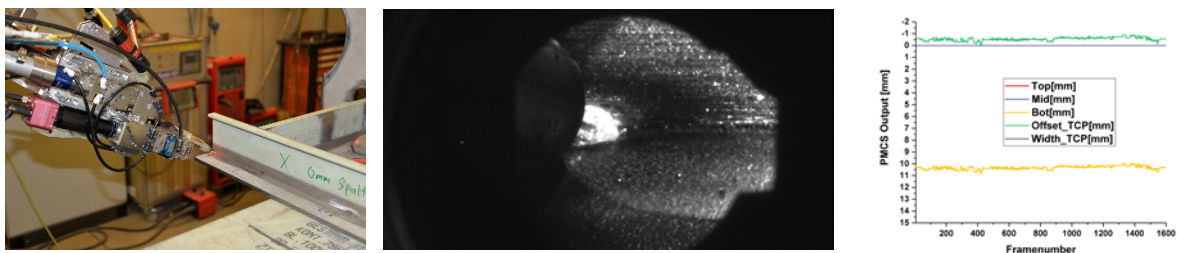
MAG Schweißprozess mit 2 kW Laserunterstützung; Stoßkonfiguration: T-Stoß mit HP-Profil als Steg; Beleuchtungsparameter: Stromstärke: 70 A, Pulsdauer: 100 μ s
